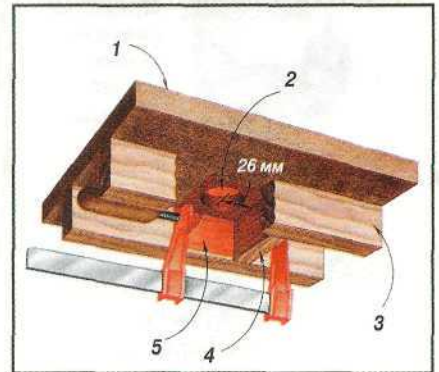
Шаблон для фрезерования гнезд для крышек:
